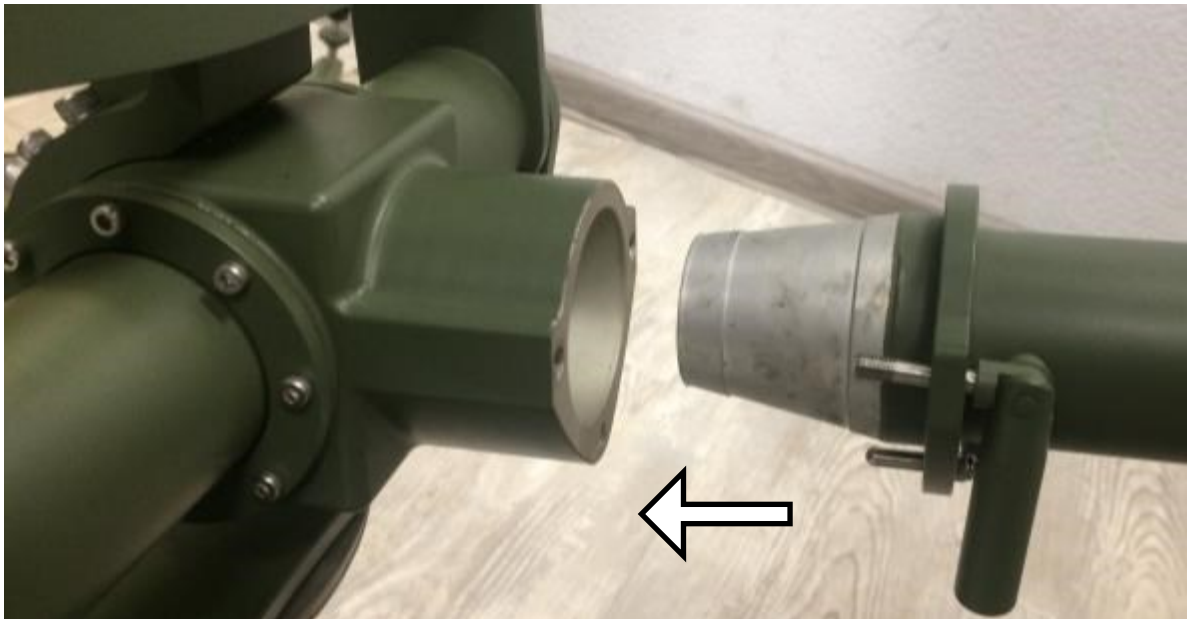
Установка держателя облучателя на опорную платформу
